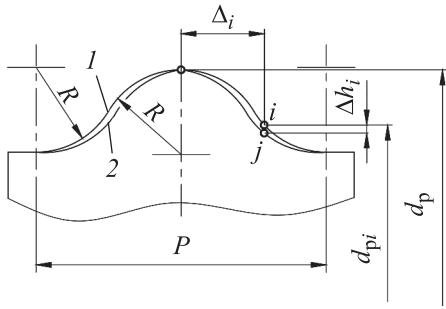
Схема профилирования резьбовой фрезы для формирования КР
